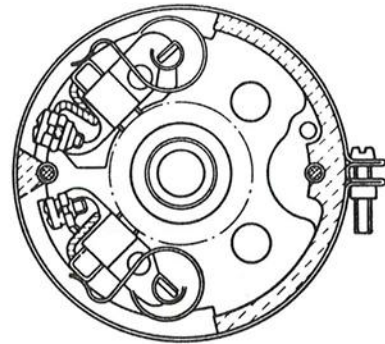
Schnitt durch das Kollektorlager mit Ansicht der Bürsten.
